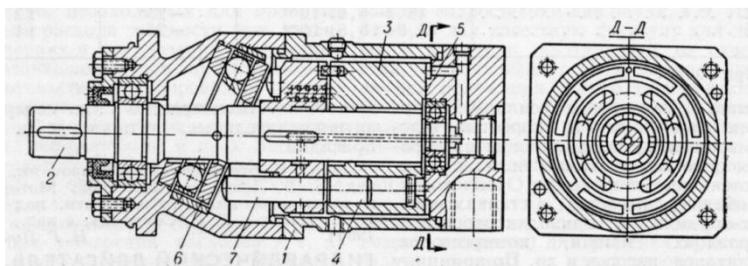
Аксиальный роторно-поршневой гидромотор:
